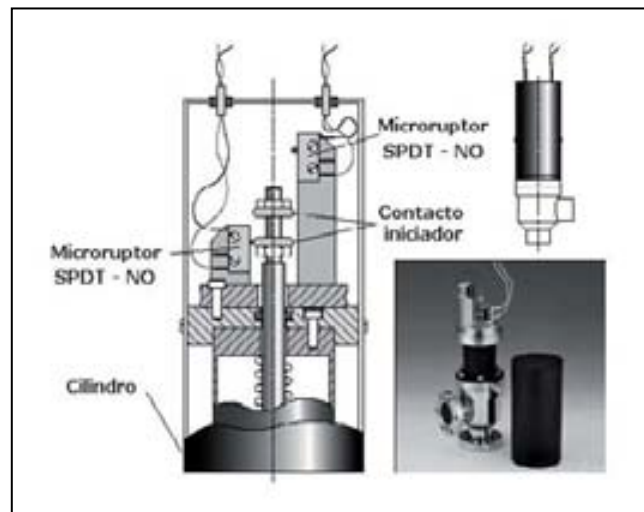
Sensor mecánico-eléctrico de final de carrera. Fuente MDC
